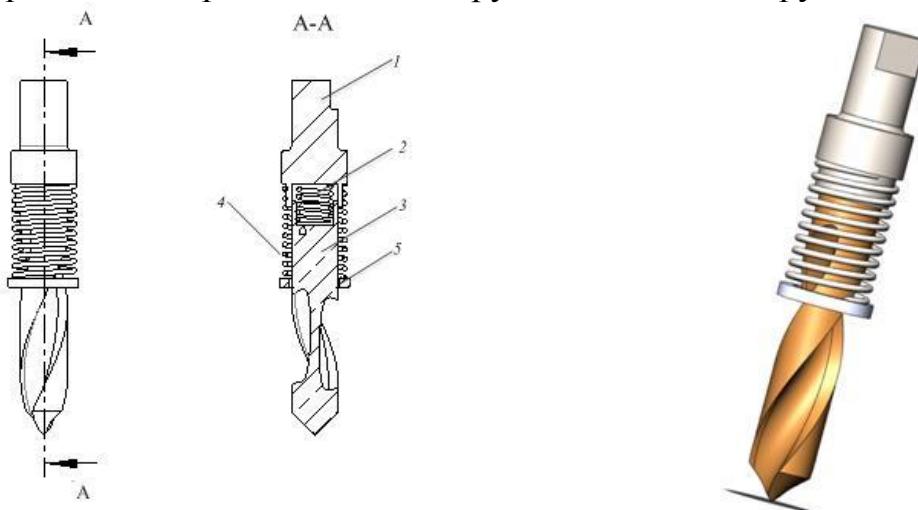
Сверло сборное для сверления ЛДСтП: 1- хвостовик, 2 - внутренний упругий элемент, 3 - режущая часть, 4 -
